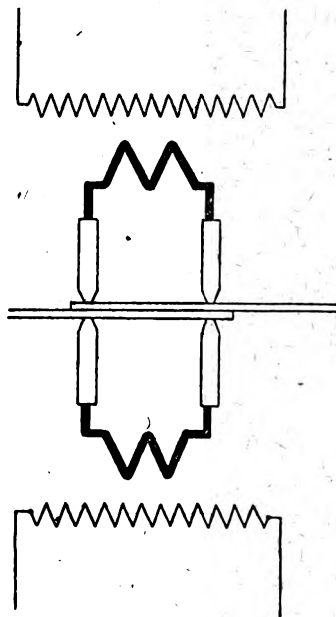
Soudure en 2 points avec 2 transformateurs.
